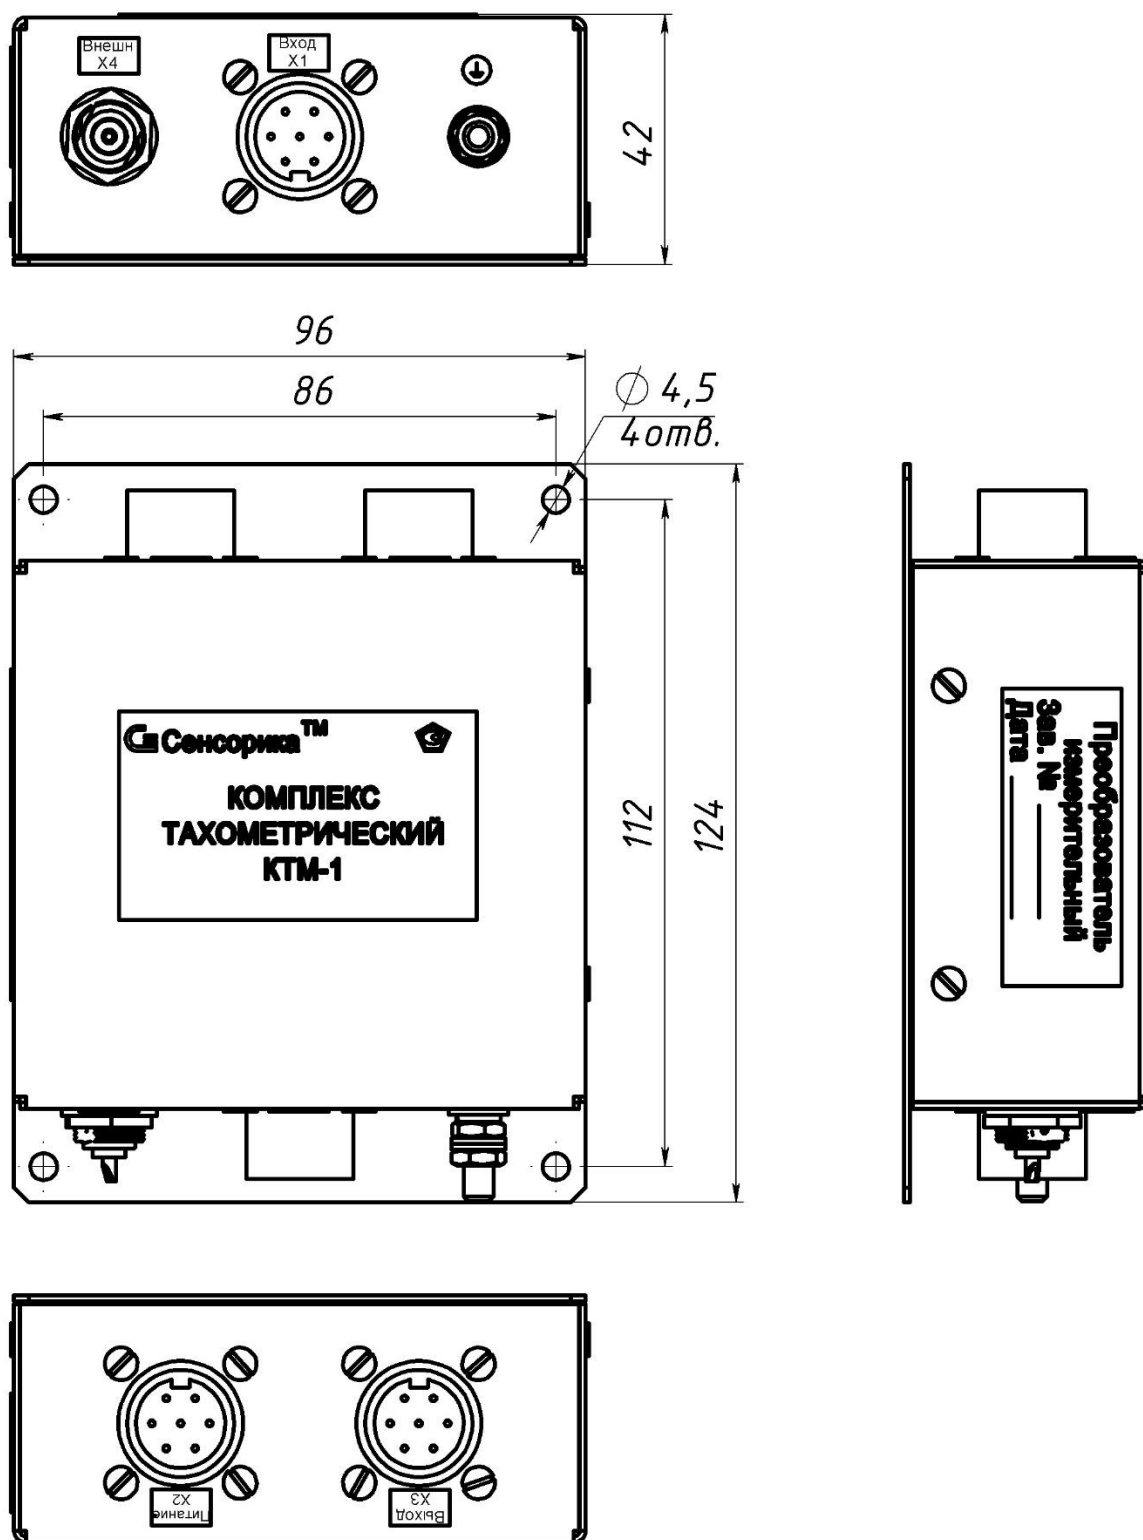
Габаритные и присоединительные размеры ДЧВ
